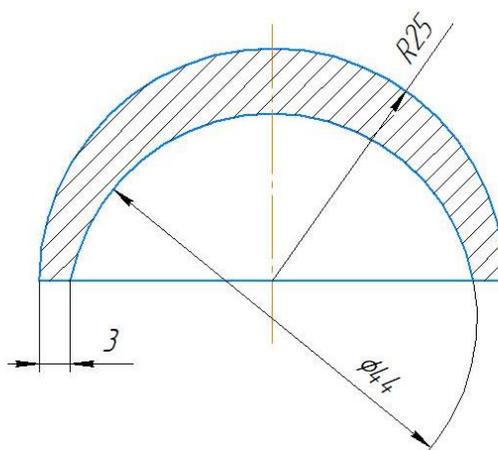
Чертеж конструкции вертлужной впадины эндопротеза
